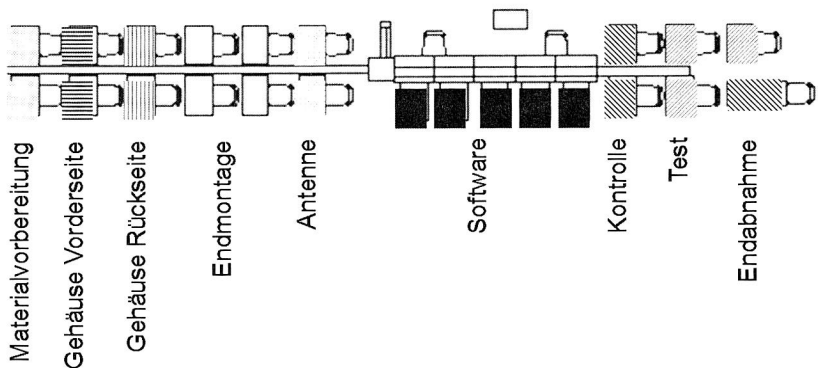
Typisches Layout einer Montagelinie für Mobiltelefone
